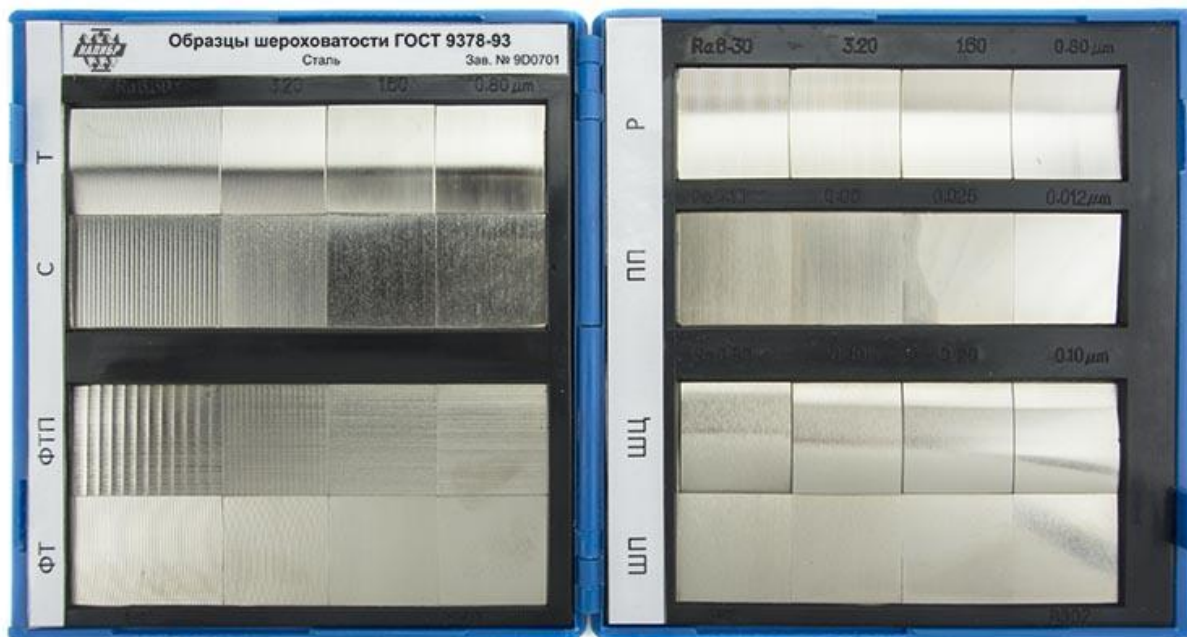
Общий вид образцов шероховатости различных видов обработки наборе в неразборной обойме
